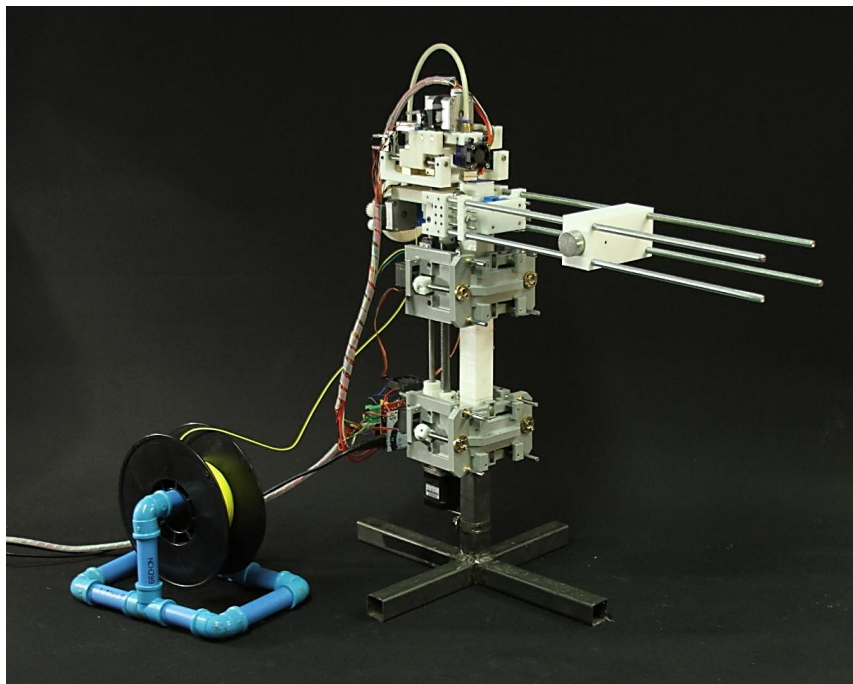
Prototipo armado sobre su base de impresión, listo para ser operado y calibrado.
